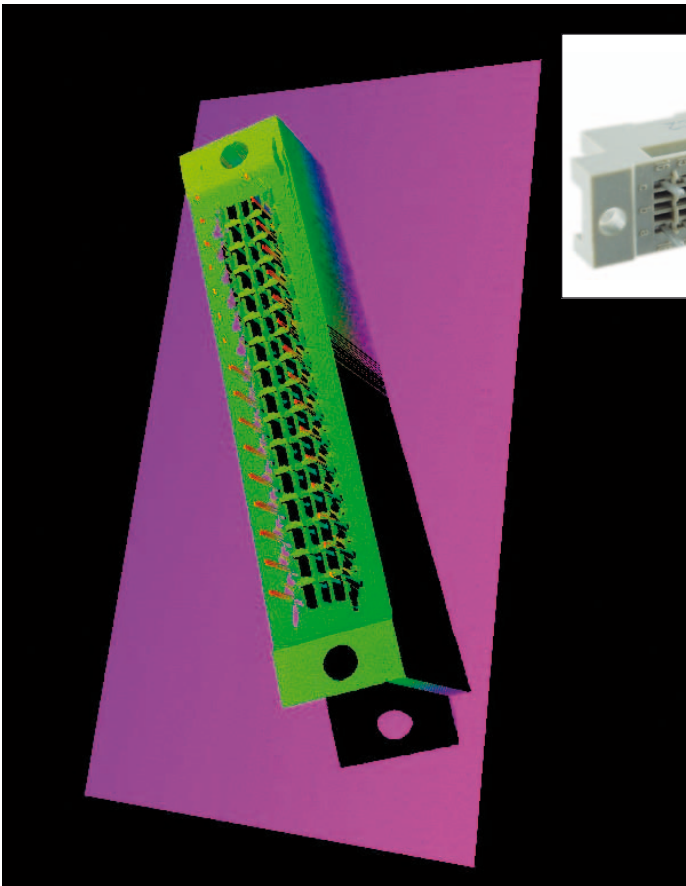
Camera Viewer mit 3D Pin-Stecker-Vermessung
